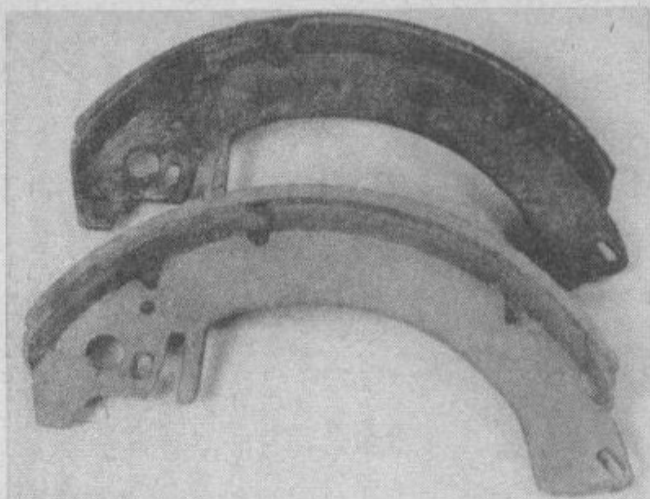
Hintere Bremsbacken des Moskwitsch 2140; oben verschlissen, unten neu
